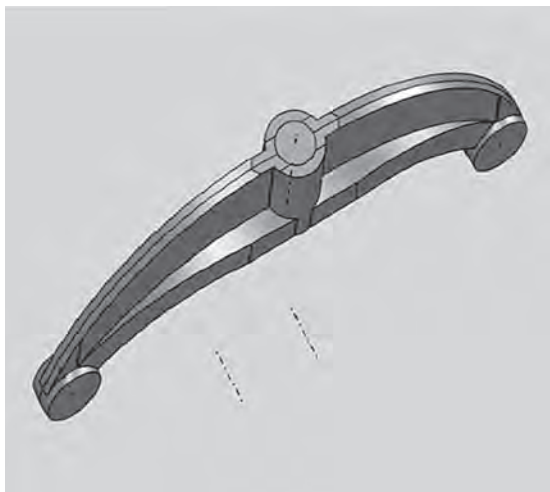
Трехмерная модель отливки «Подвес ПНД»
